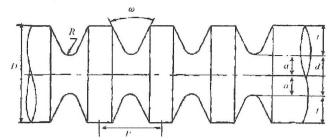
Цилиндрический образец с надрезами Vобразного профиля
